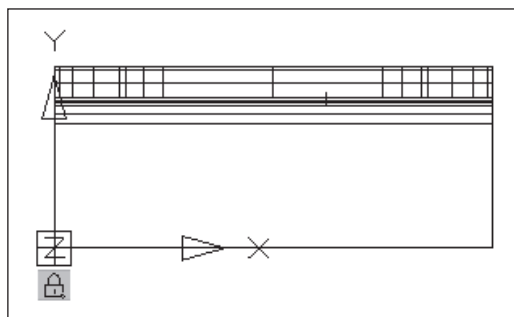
Вид 3D-модели детали «Скоба» после выбора плоскости для отверстий
